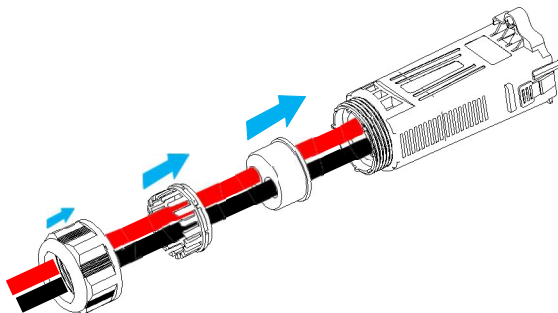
Pase el cable de la batería y monte la cubierta protectora
